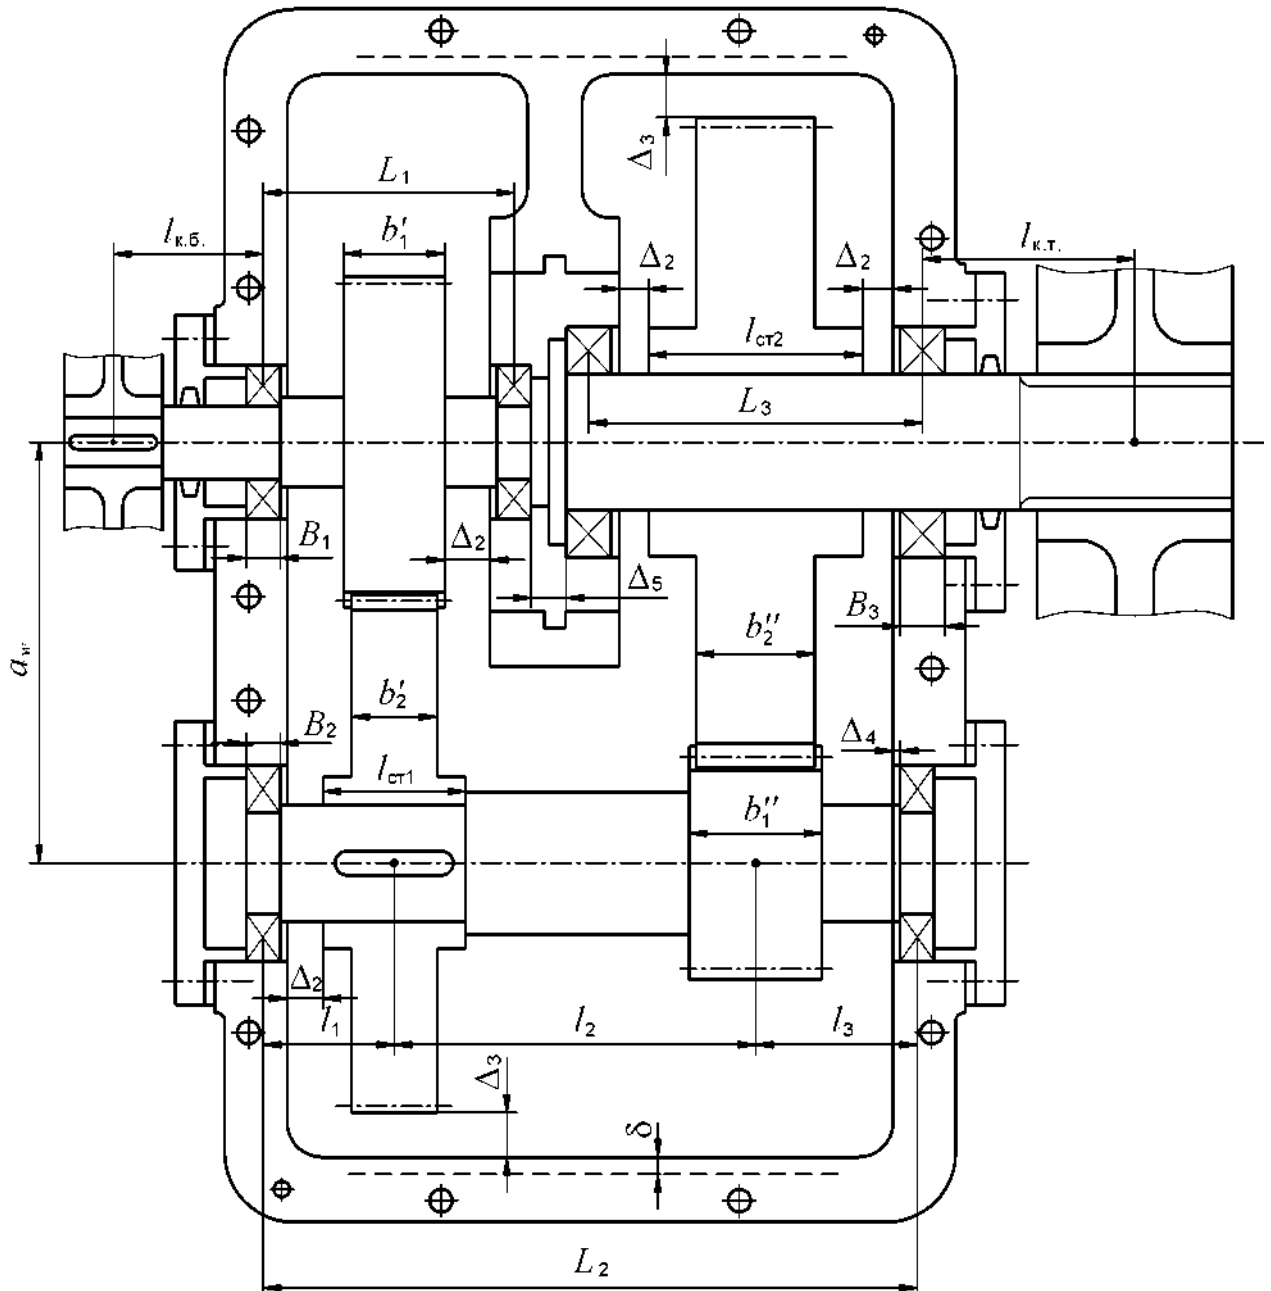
Эскизная компоновка двухступенчатого соосного редуктора
